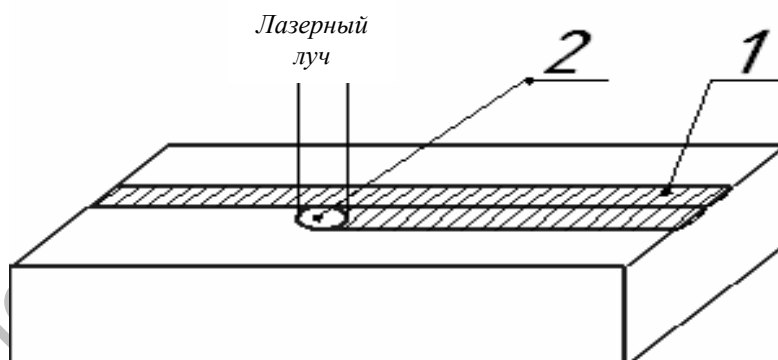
Лазерная закалка металла: 1 – зона закалки; 2 – пятно фокусировки лазерного излучения
